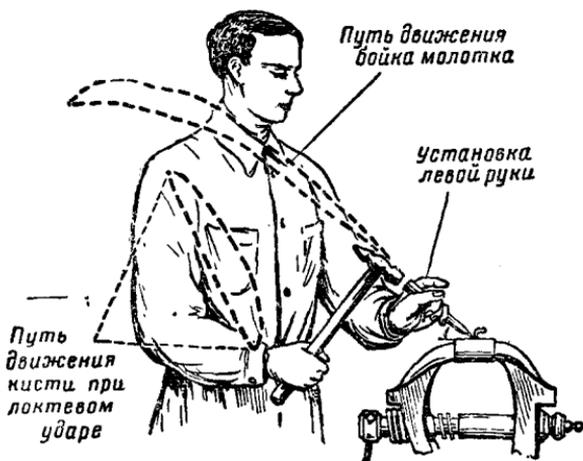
Положение корпуса слесаря при рубке зубилом в тисках.
